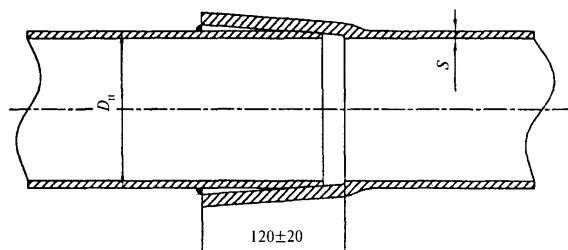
Схема сварного нахлестного соединения
